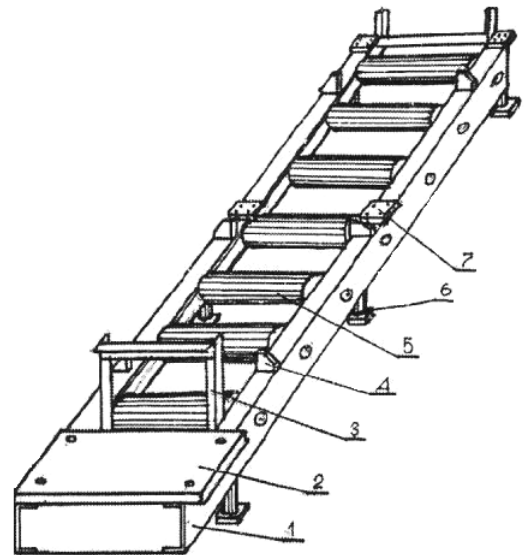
Схема загального виду транспортера: 1 – рама, 2 – плита для установки приводу, 3 – напрямна для касети 4 – упор; 5 – ролики; 6 – регульована опора; 7 – платина
